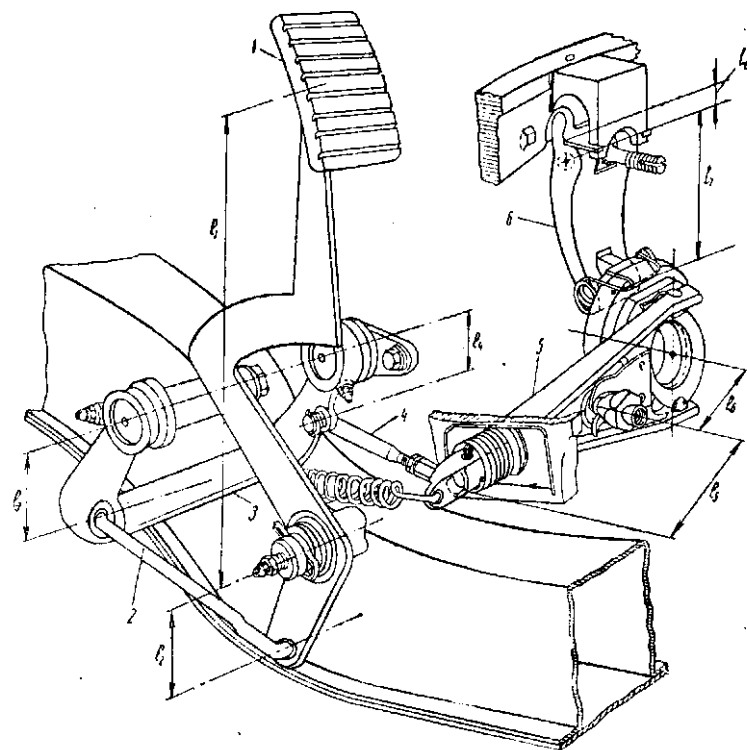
Схема механизма привода выключения сцепления: 1— педаль; 2— тяга; 3— скоба выключения; 4 — толкатель вилки выключения сцепления; 5 — вилка выключения сцепления; 6 — отжимной рычаг механизма сцепления
